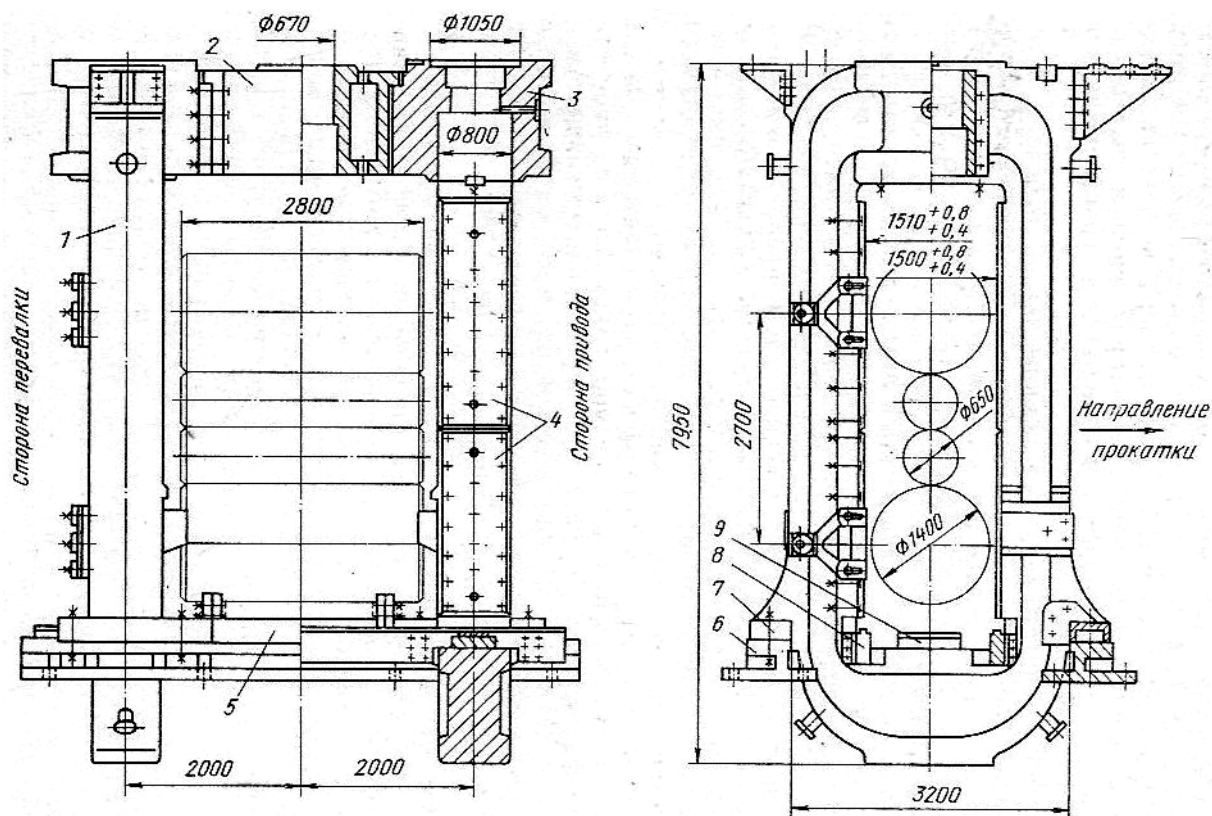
Узел станин рабочей клетки 2800 стана горячей прокатки ПОЛОС
